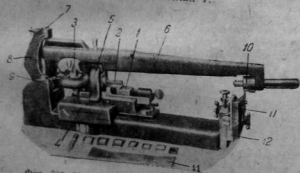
Удешевленный копировальный горизонтально-фрезерный станок с делительным диском.
